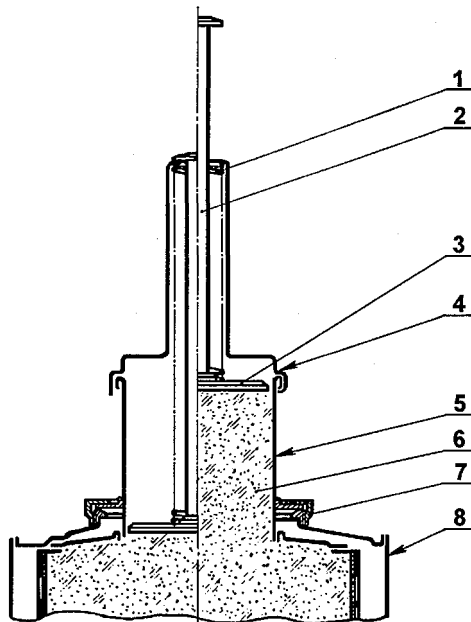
Уплотнитель ХП-И (приспособление для снаряжения патрона регенеративного)
